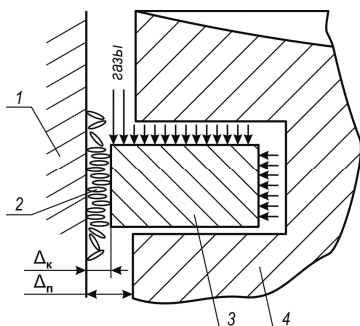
Модель трибологической системы цилиндровой втулки – смазочный материал – поршневое кольцо: 1 – втулка цилиндра; 2 – смазочный материал; 3 – кольцо; 4 – поршень
